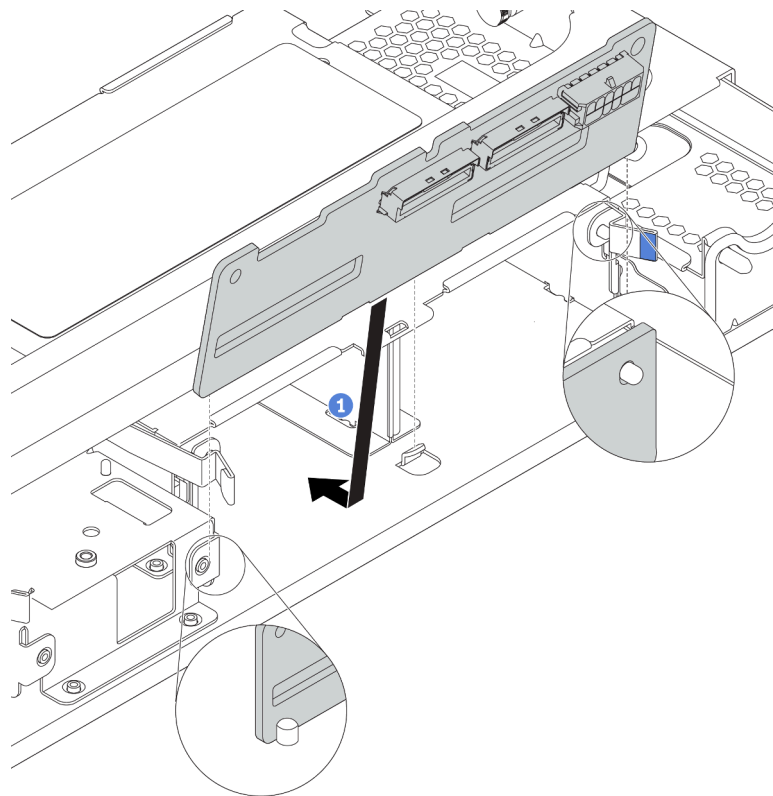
Installation du fond de panier d'unité 2,5 pouces central ou arrière
